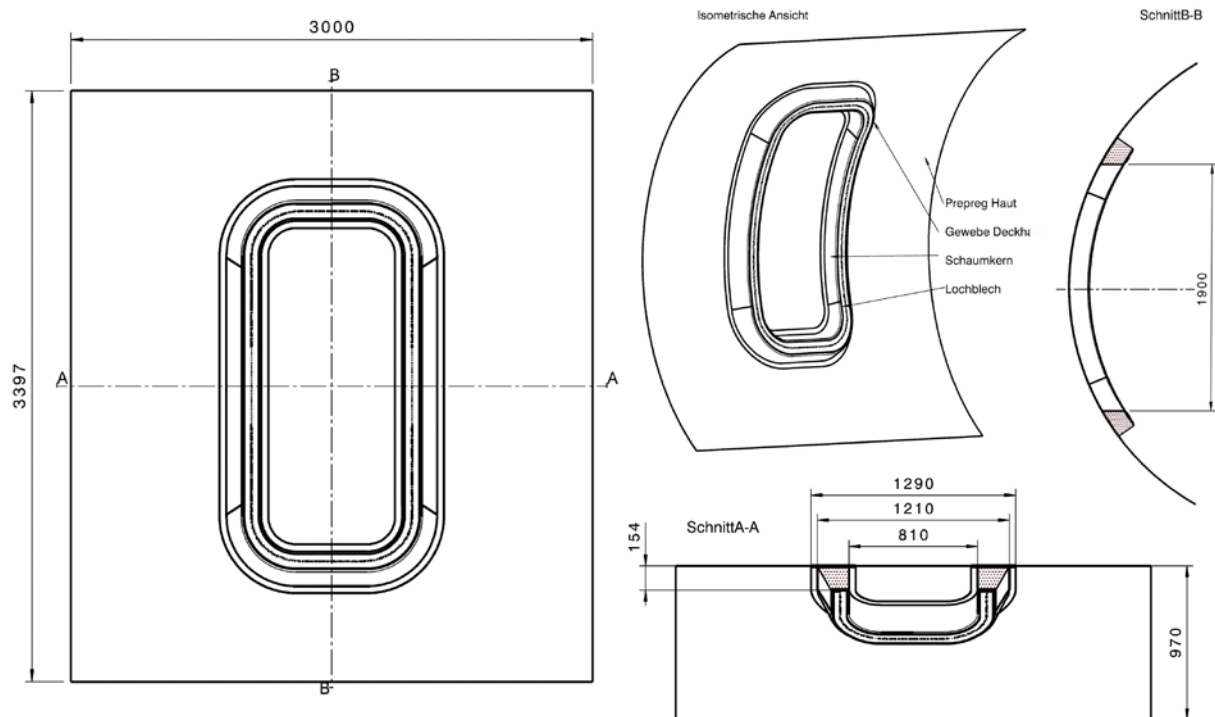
Auslegung und Dimensionen des Türrahmendemonstrators in kombinierter Prepreg-Nasstechnologie
